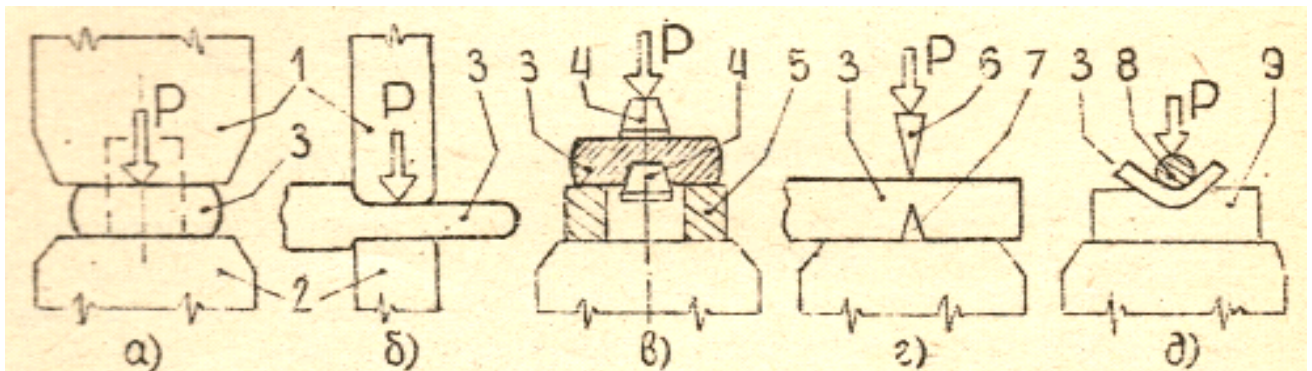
Операцииковки: 1 и 2 — верхний и нижний бойки; 3 — поковка; 4 — прошивень; 5 — подкладное кольцо; 6 — топор; 7 — надрез; 8 — оправка; 9 — подкладной штамп
